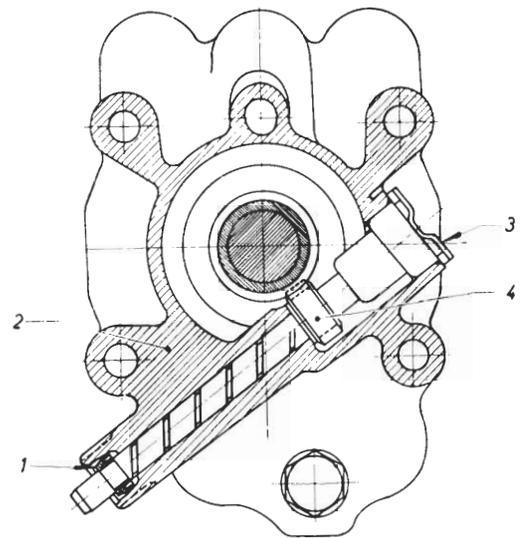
Tachometerschraubenrad in Getriebegehäuseendstück eingebaut
